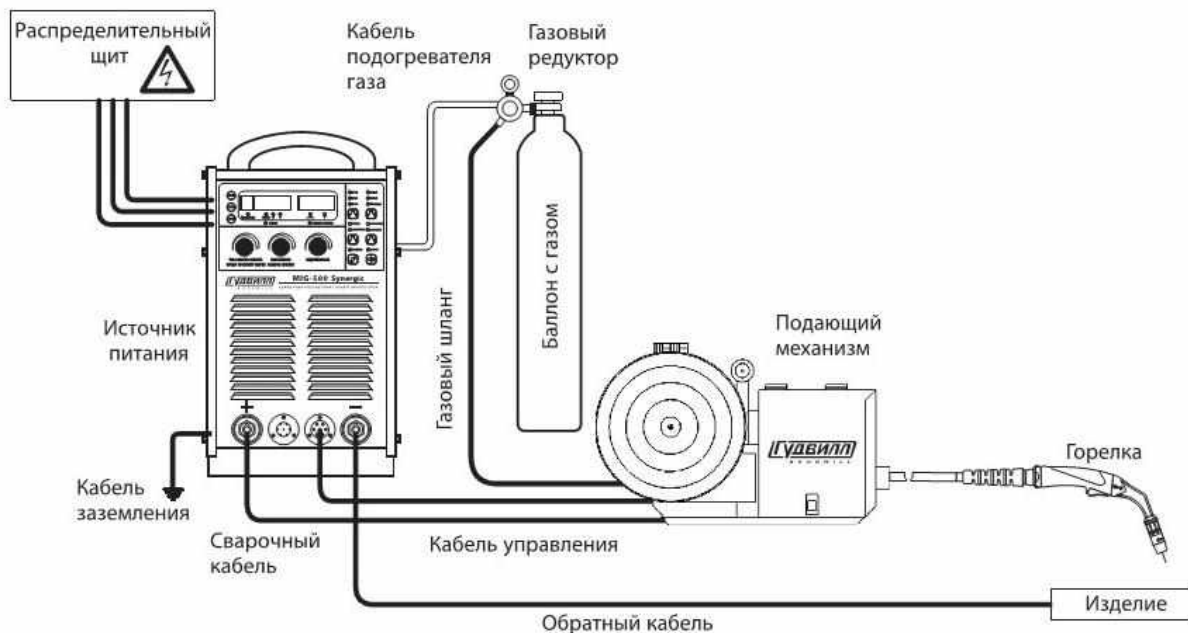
Комплект сварочного оборудования для MIG/MAG сварки
